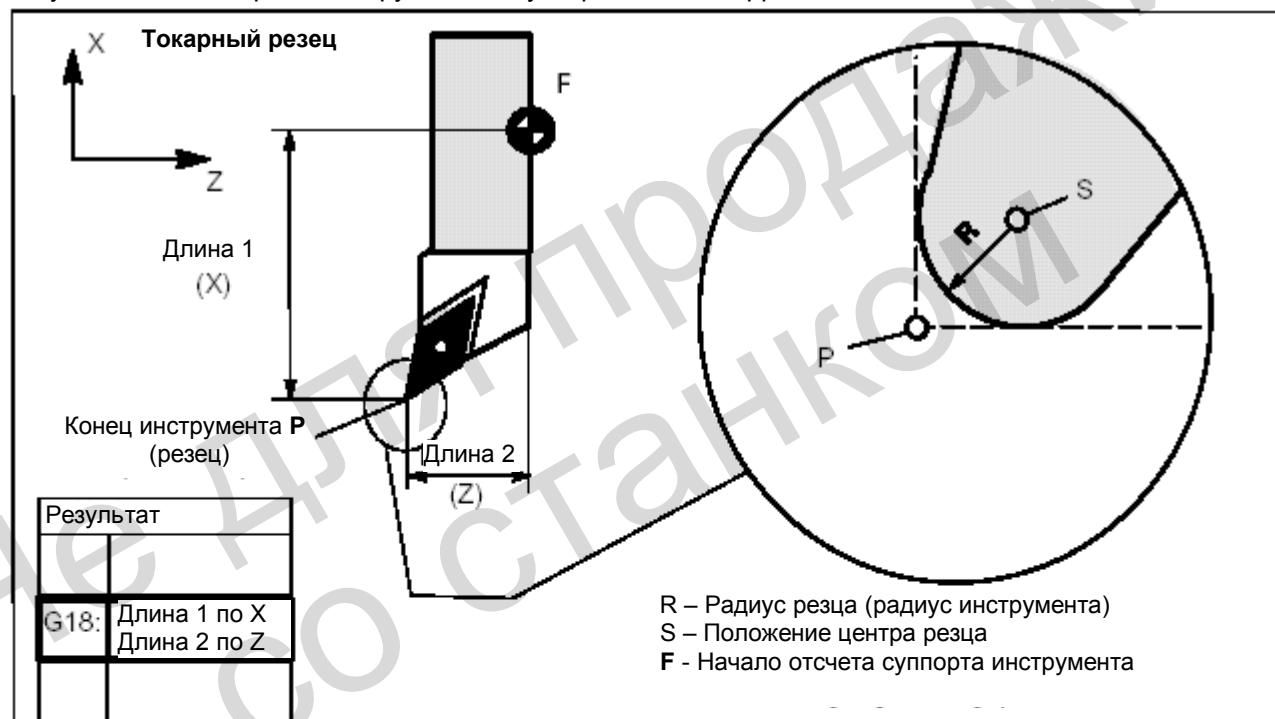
Токарный инструмент с двумя резцами – Коррекция длины
